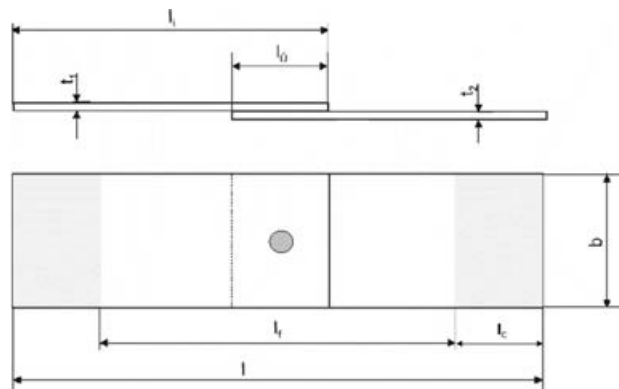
Skizze der einschnittig überlappten Scherzugprobe.
